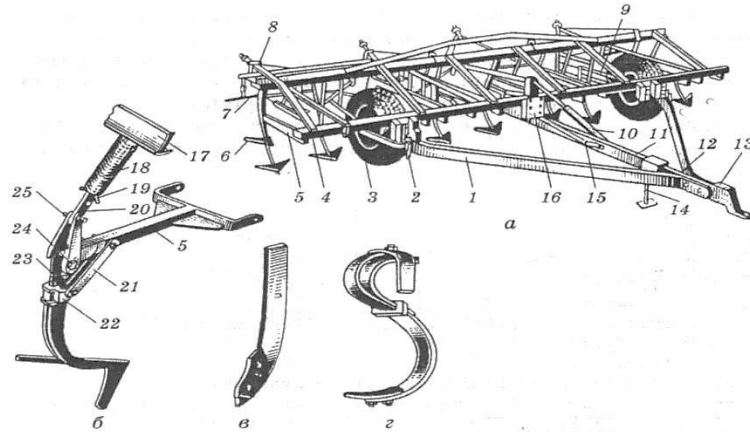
Культиватор причіпний для суцільного обробітку ґрунту КПС-4: а — загальний вигляд; б — стрілчаста лапа; в, г — розпушувальні лапи; 1 і 12 — бічні бруси сніці; 2 — регулятор глибини; 3 — опорне колесо; 4 — рама; 5 і 9 — гряділі; 6 — лапа; 7 — повідець; 8 — начіпний механізм для борін; 10 — гідроциліндр 11 — сніця; 13 — причіпний пристрій; 14 — підставка; 15 — транспортна тяга; 16 — стовпа; 17 — кутик рами; 18 — пружина; 19 — шплінт; 20 — штанга; 21 — планка; 22 — утримувач; 23 — 25 — болтові з'єднанняєорганів 2.
